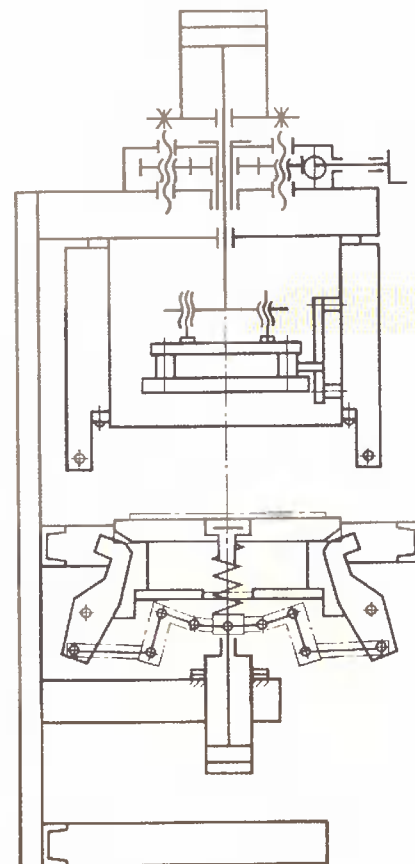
Сварочный пресс с разгрузочной консолью
